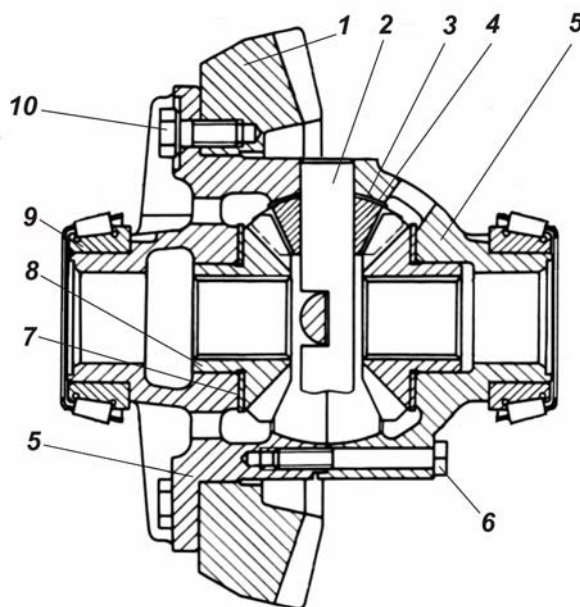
Дифференциал в сборе с ведомой шестерней: 1 – шестерня ведомая; 2 – ось сателлитов; 3 – шайба сателлитов; 4 – сателлит; 5 – коробки сателлитов; 6, 10 – болты; 7 – шайба шестерни полуоси; 8 – шестерня полуоси; 9 – подшипник
